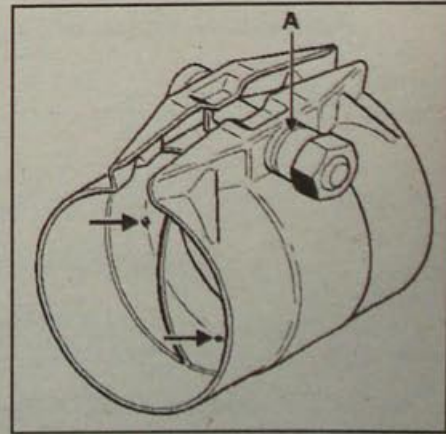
Ремонтный патрубок системы выпуска отработавших газов: А — канавка, определяющая момент затяжки гайки
